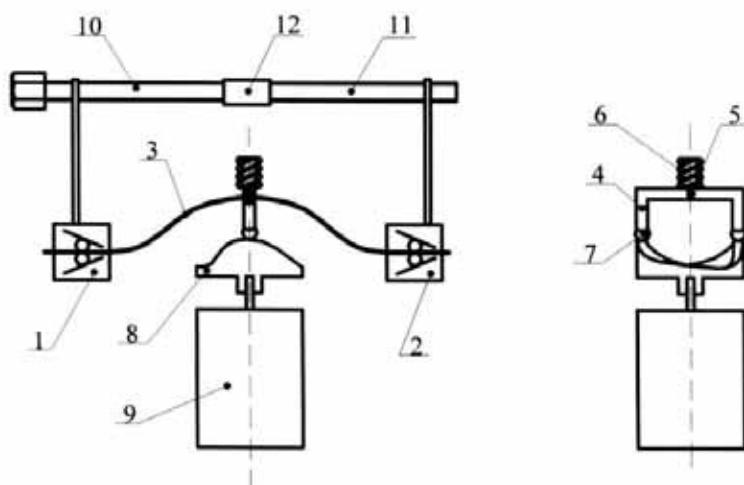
Механизм импульсной подачи с квазиволновым движением проволоки, имеющий плоский кулачок: 1,2 – зажим; 3 – проволока; 4 – шток; 5 – отверстие; 6 – пружина; 7 – ролик; 8 – кулачок
